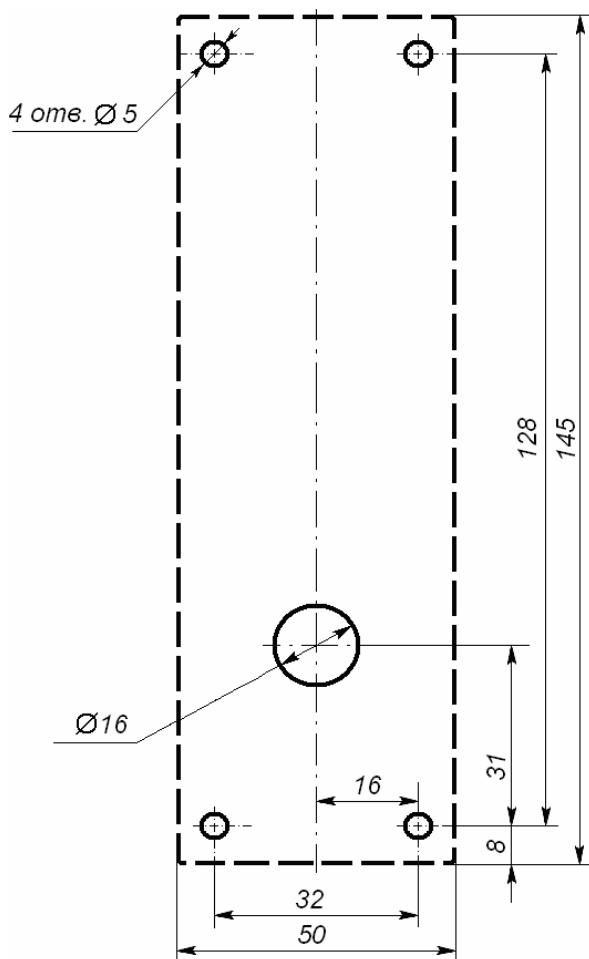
Разметка отверстий для установки считывателя (пунктиром показаны габариты корпуса считывателя)
